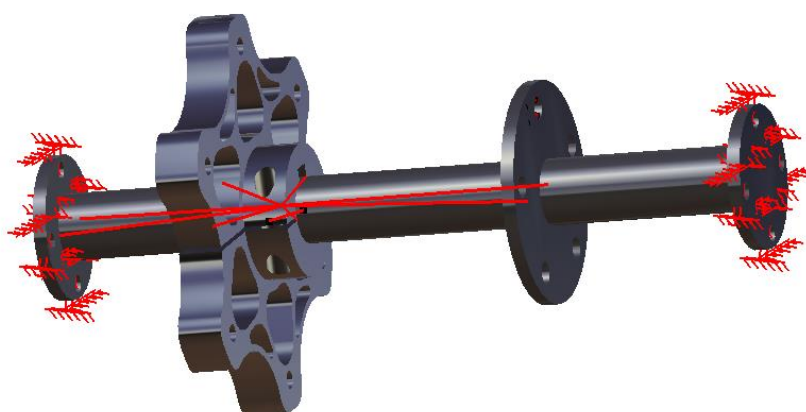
Aplicação de restrição e carregamento para a análise do eixo de tração.
